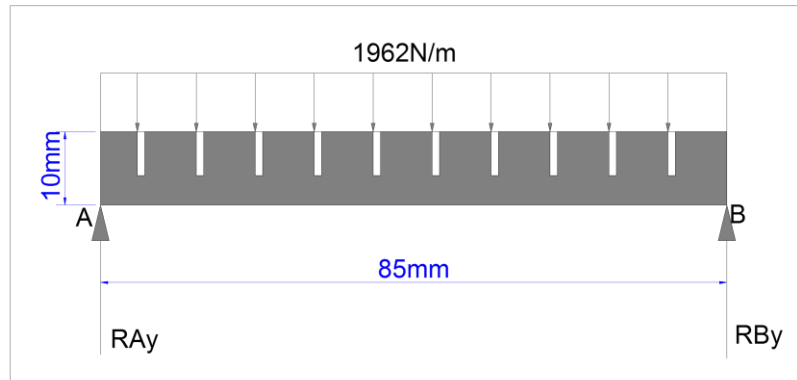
Dimensionamiento de espesor cuchilla tipo rejilla. (0.7mm)
